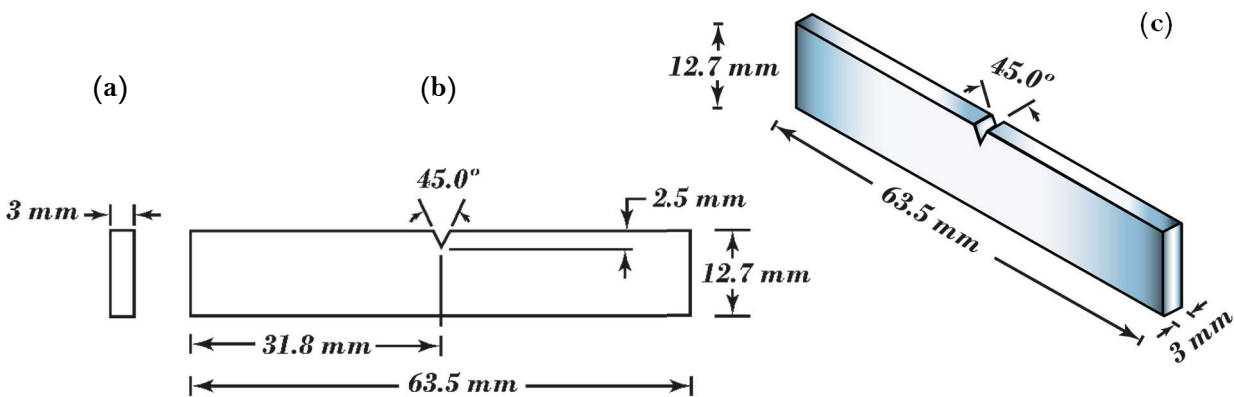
Dimensiones de la probeta para ensayo de impacto: (a) Espesor del espécimen; (b) Vista frontal; (c) Vista isométrica.
